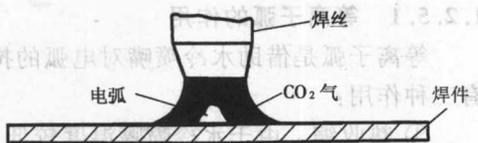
CO₂ 气体保护焊的工作原理图
